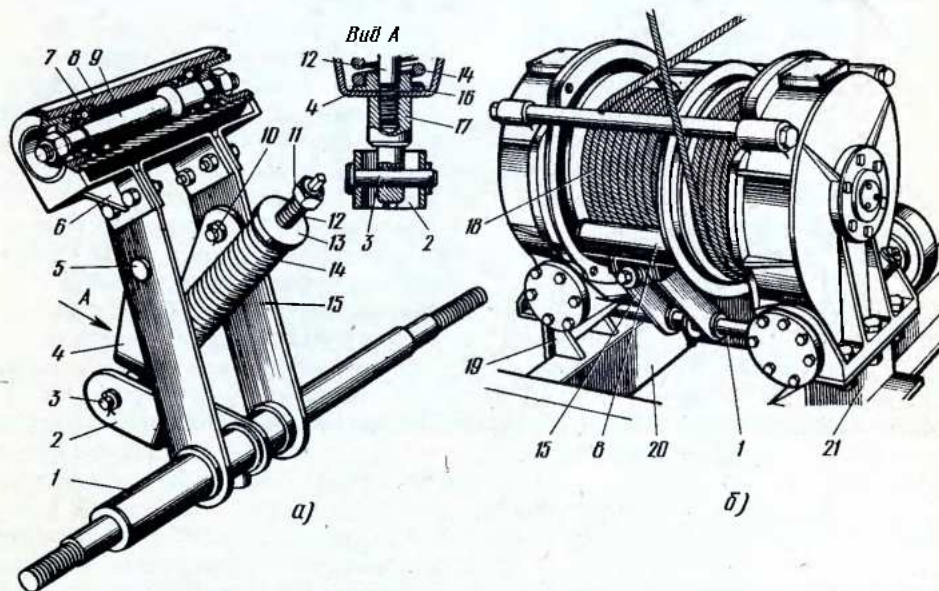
Прижимной ролик грузовой лебедки крана (а) и его установка на поворотной платформе (б):
